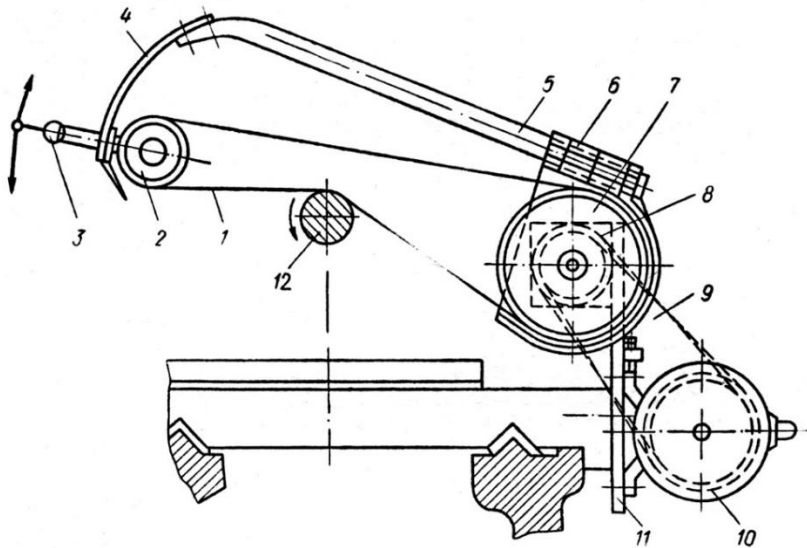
Схема пристрою для полірування деталей безкінечною стрічкою: 1 – безкінечна стрічка; 2 – ролик; 3 – рукоятка; 4 – пружна пластина; 5 – стержень; 6 – кронштейн; 7 – шків; 8 – вібратор; 9 – клинопасова передача; 10 – електродвигун; 11 – плита; 12 – деталь
